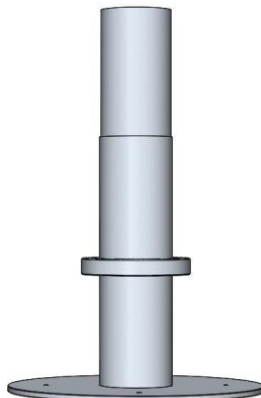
Загальний вигляд несучої опорної конструкції
